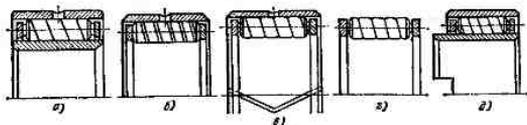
Роликоподшипники с витыми роликами типов: а — 5000; б — 35000; в — 45000; г — 65000; д — 15000
